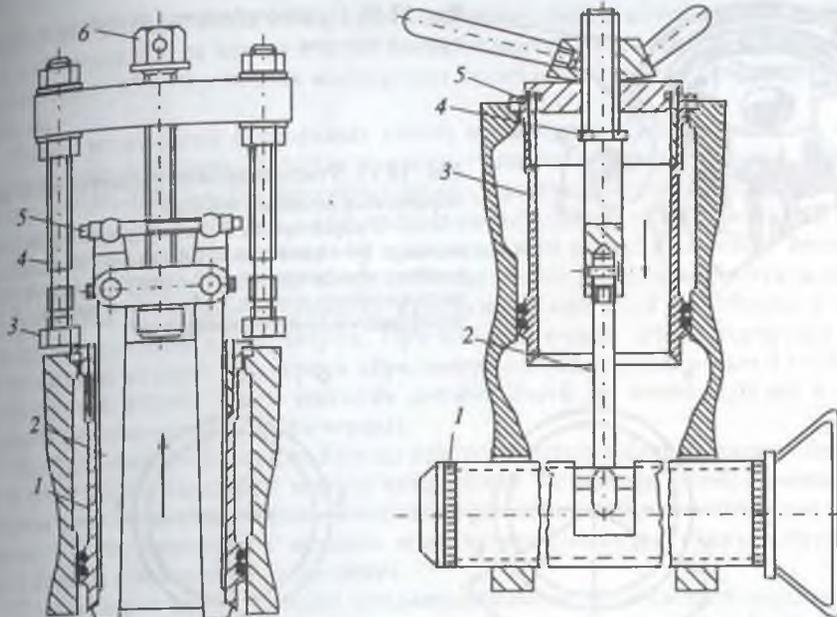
Комбинированный съемник для выпрессовки гильзы из блока цилиндров
